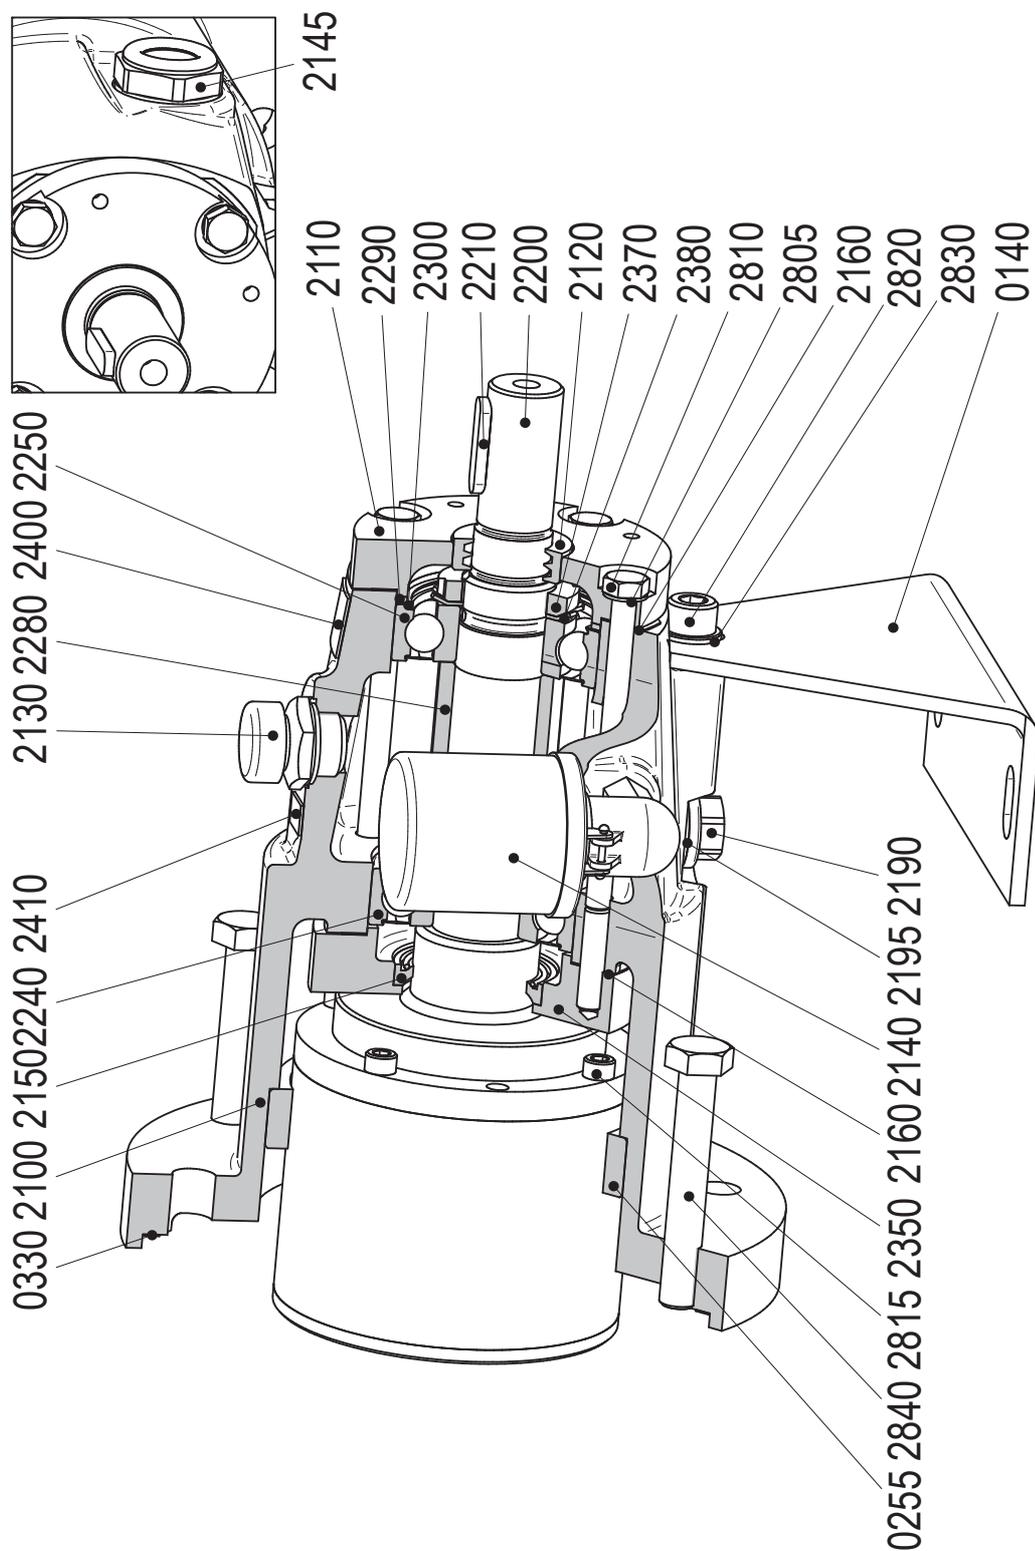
Роликовый подшипник L3 с масляной смазкой, MAG 75
